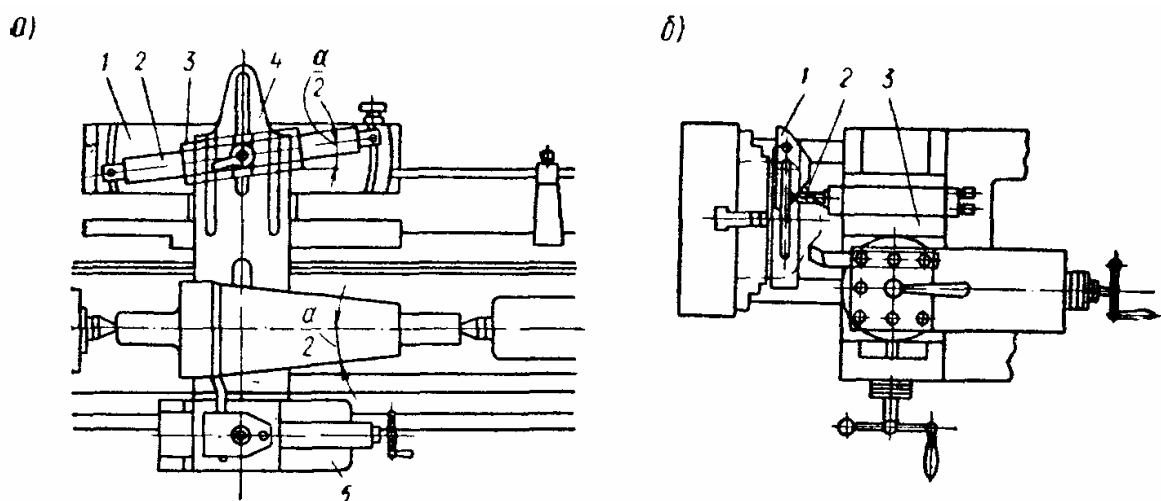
Обработка на токарном станке сложных поверхностей с помощью копиров с настроенными кинематическими цепями
